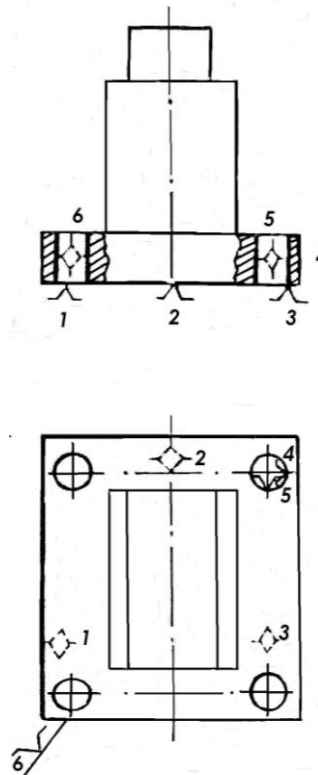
Схема базирования заготовки «Корпус».
